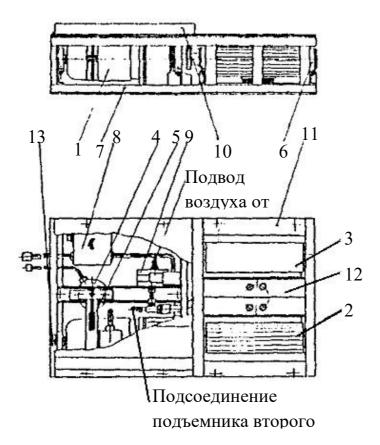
Блок роликов: 1 – мотор-редуктор; 2 – ведущий ролик; 3 – поддерживающий ролик; 4 – датчик силоизмерительной системы; 5 – рычаг; 6 – опоры; 7 – рама; 8 – коробка; 9 –
